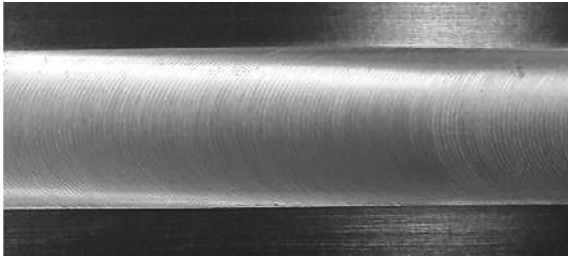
Внешний вид шва, полученного сваркой трением с перемешиванием на сплаве 1565ч
